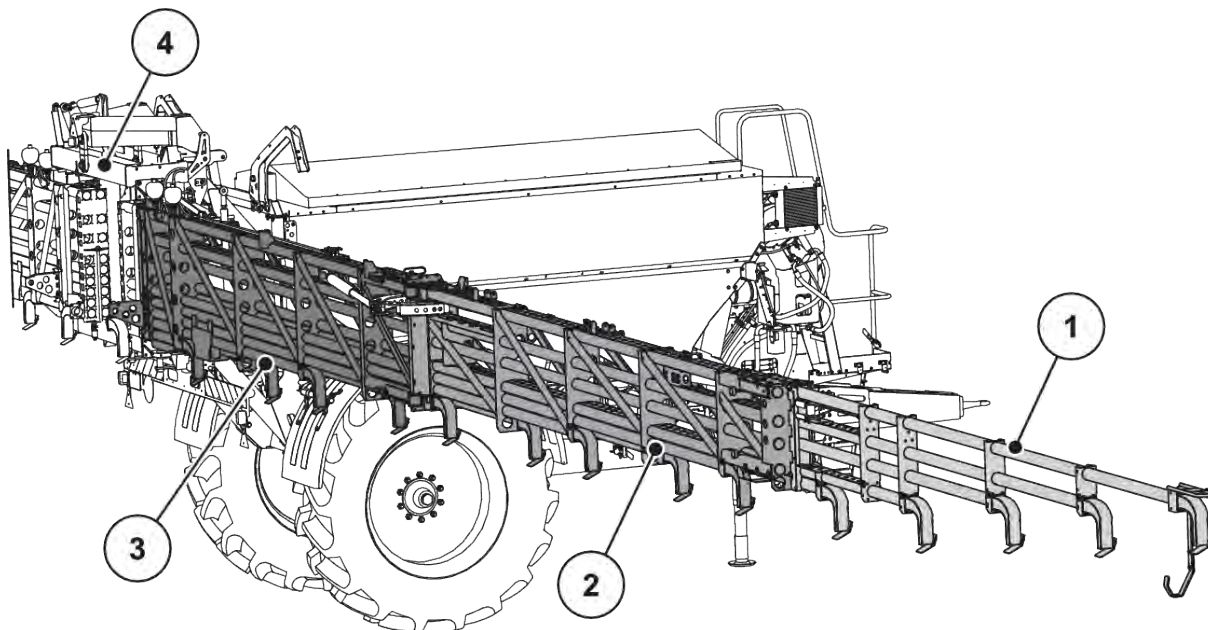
Baugruppen und Funktionen der Maschine, Ausleger
